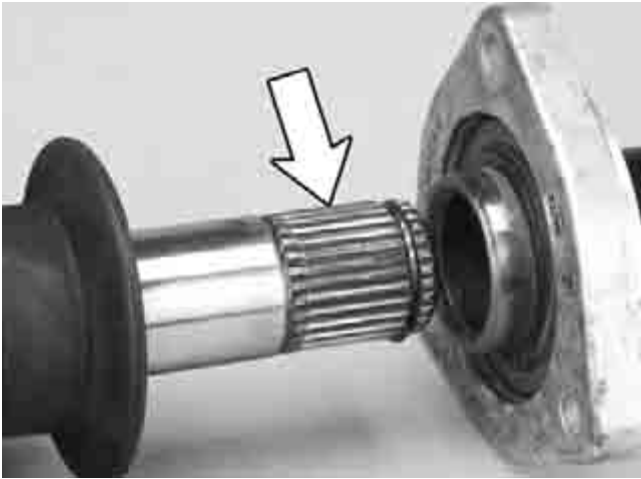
Место нанесения смазки в месте соединения приводного вала.
